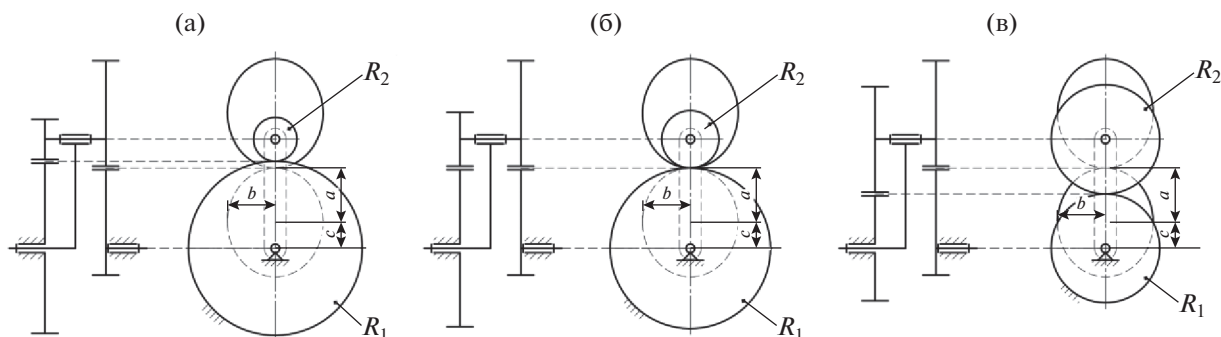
Варианты планетарного механизма с эллиптическими зубчатыми колесами для различных видов движения: (а) – неравномерное движение; (б) – движение с остановками; (в) – возвратно-вращательное движение;  $a$ ,  $b$ ,  $c$  – большая полуось, малая полуось и фокальное расстояние эллипса;  $R_1$  и  $R_2$  – радиусы цилиндрических зубчатых колес.
